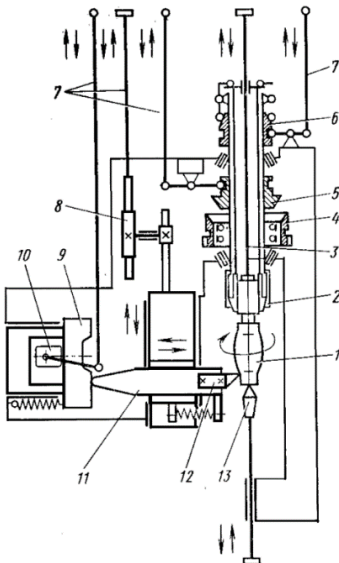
Схема робочого органу ротора для обробки деталей типу тіл обертання
